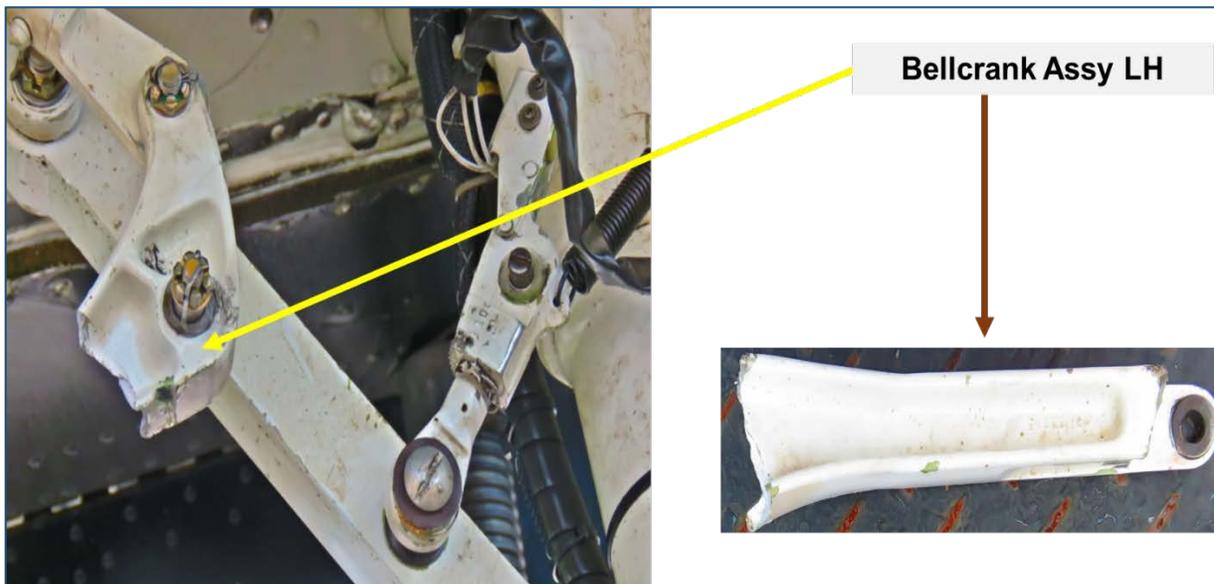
Fracturas y pérdida de material en flap izquierdo.
